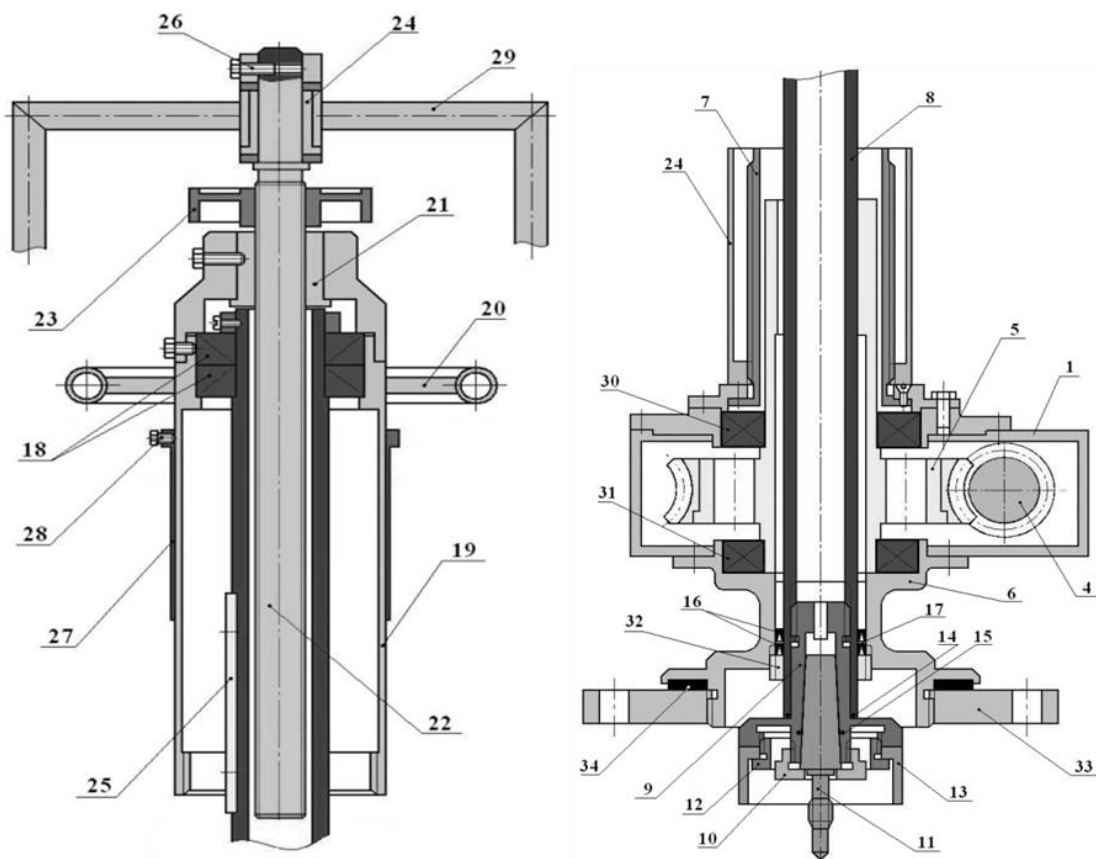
Прорезное устройство АКВ-103 «Пирания». 1 - корпус редуктора, 2 - электродвигатель, 3 - муфта электродвигателя, 4 - червяк, 5 - червячное колесо, 6 - резьбовой корпус, 7 - винт основной подачи, 8 - шпиндель, 9 - переходник, 10 - гайка, 11 - сверло – метчик, 12 - гайка, 13 - фреза, 14,15 - кольцо резиновое, 16 - манжета, 17 - шайба, 18 - подшипник, 19 - гайка – стойка, 20 - маховик, 21 - гайка, 22 - винт быстрой подачи, 23 - маховик, 24 - кожух, 25 - шпонка, 26 - гайка, 27 - шаблон, 28 - болт, 29 - стойка, 30, 31 – подшипник, 32 - гайка, 33 - фланец, 34 – прокладка
